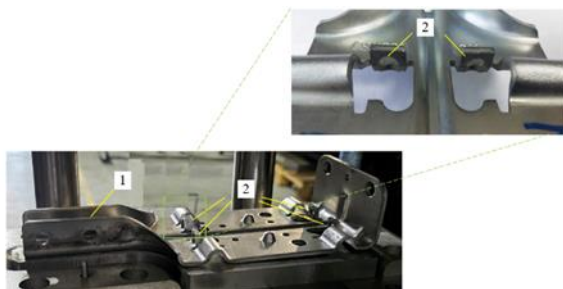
Внешний вид детали «кронштейна роликовой» тележки:
